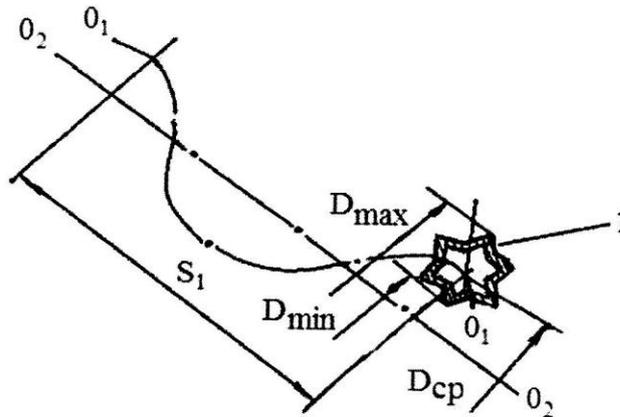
Схема изготовления рабочего органа 1 станка для шлифования, полирования и упрочнения поверхностного слоя деталей:
